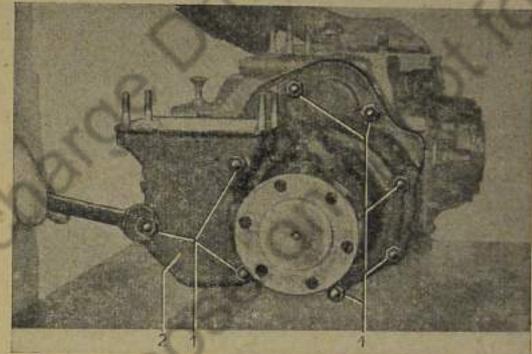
Schaltgehäuse vom Getriebe abschrauben
